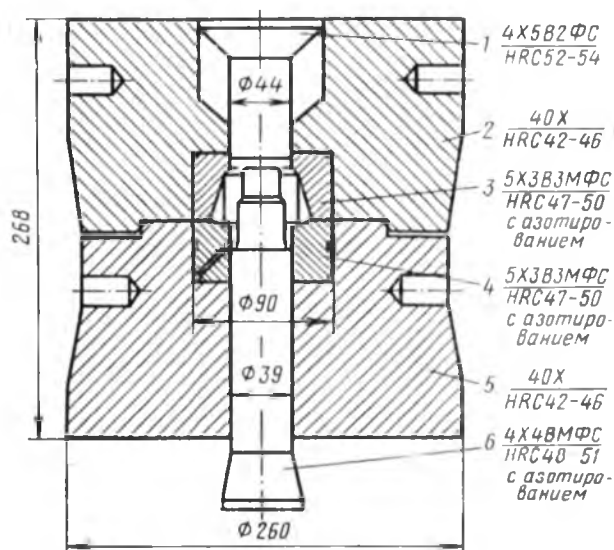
Марки стали и нормы твердости основных деталей штампа КГШП для выдавливания в разъемных матрицах поковок типа стакана с ребрами:
